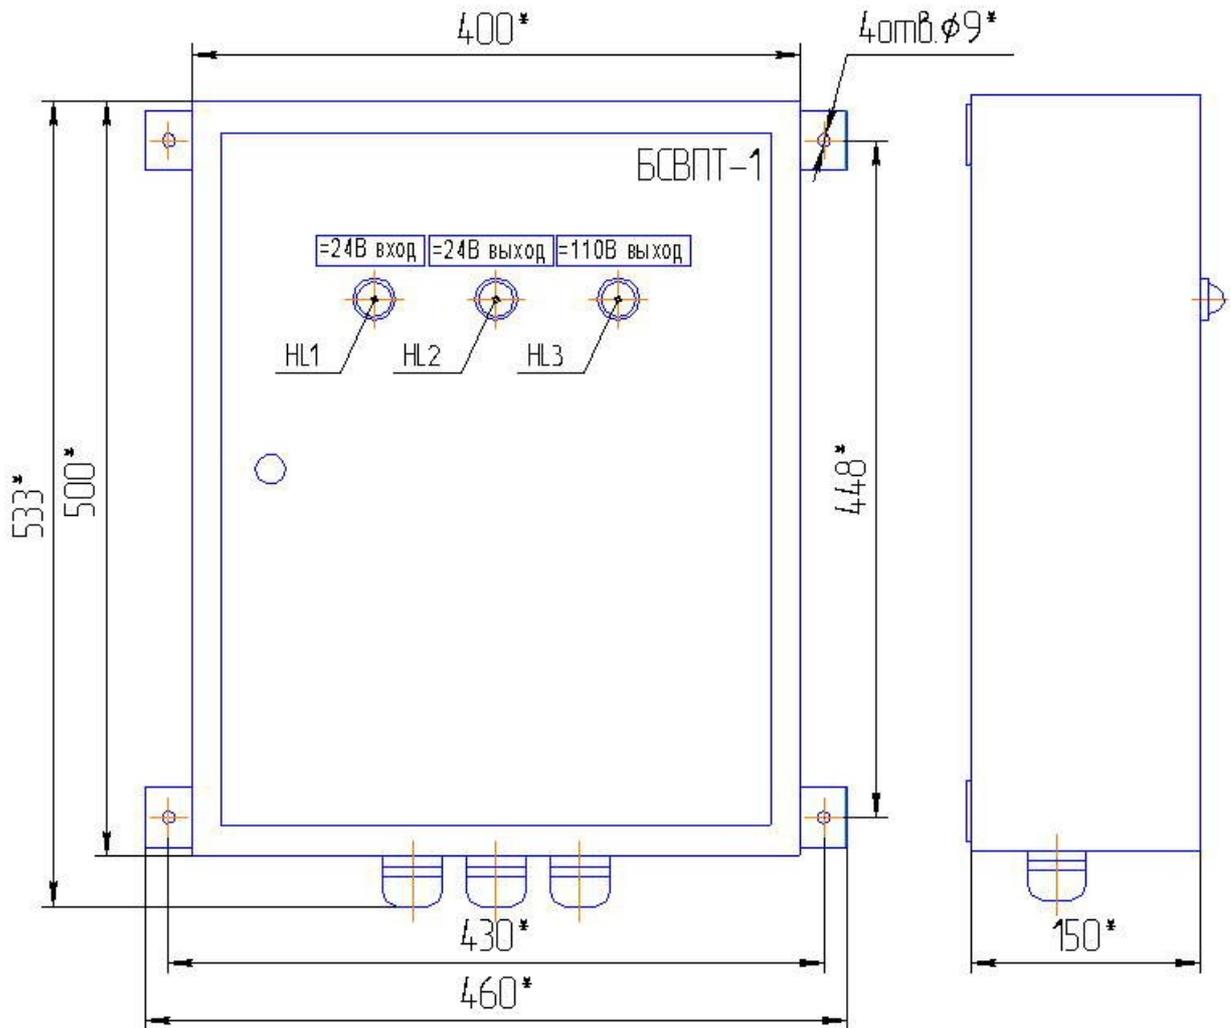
Габаритный чертеж БСВПТ-1
